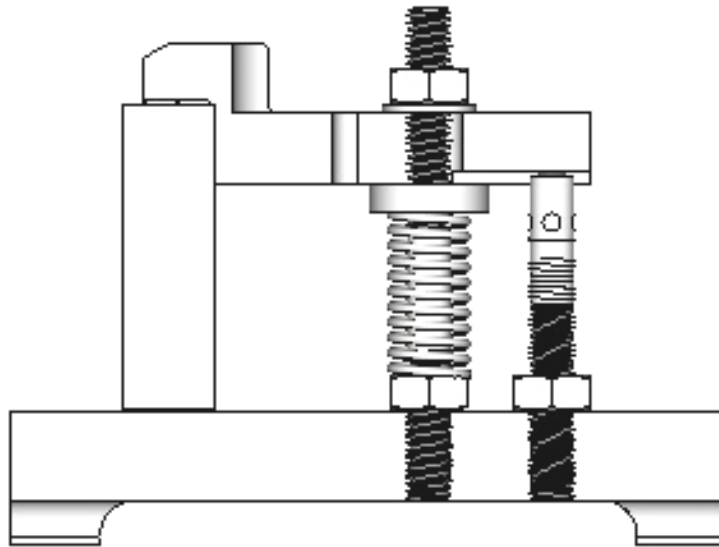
Конструкция зажимного устройства с прихватом ступенчатым
